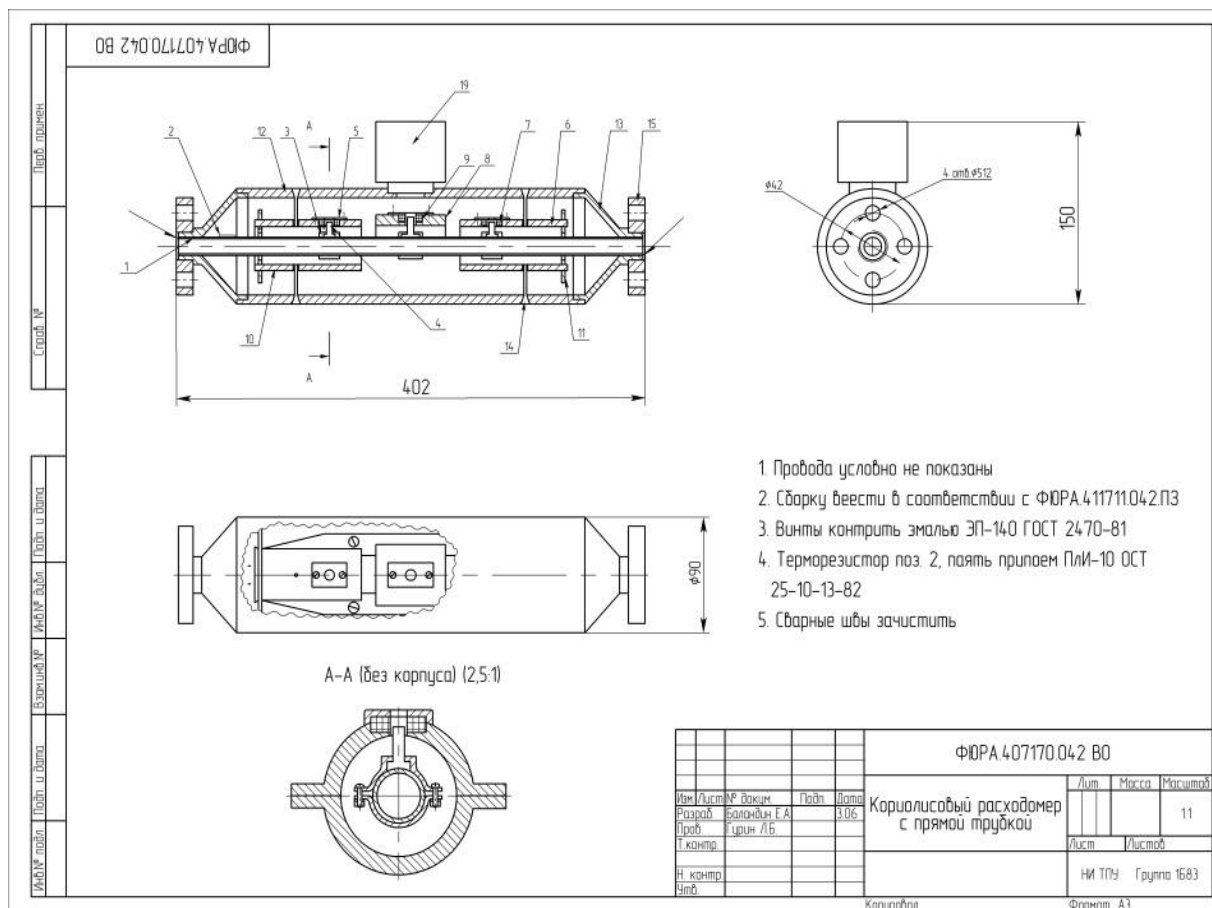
Сборочный чертеж расходомера с прямой трубкой
